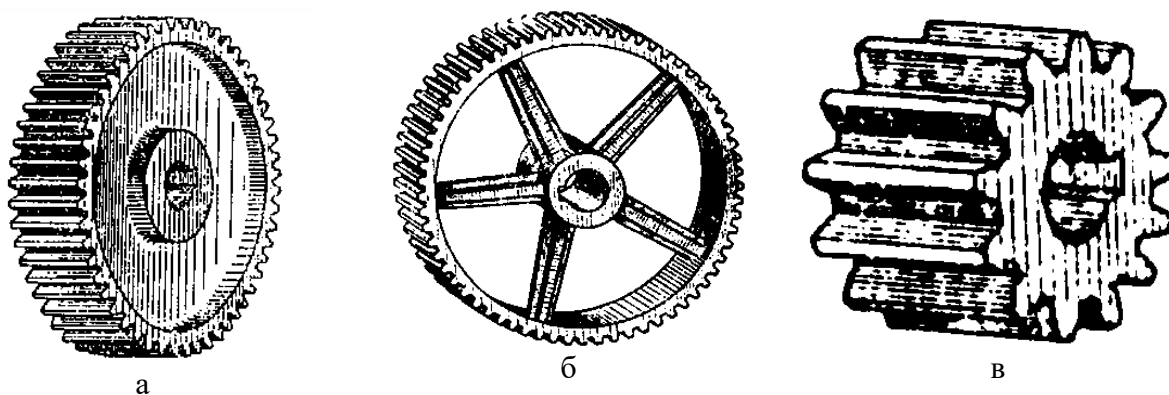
Виды зубчатых колес: а – дисковое зубчатое колесо; б – зубчатое колесо со спицами; в – сплошное зубчатое колесо.
